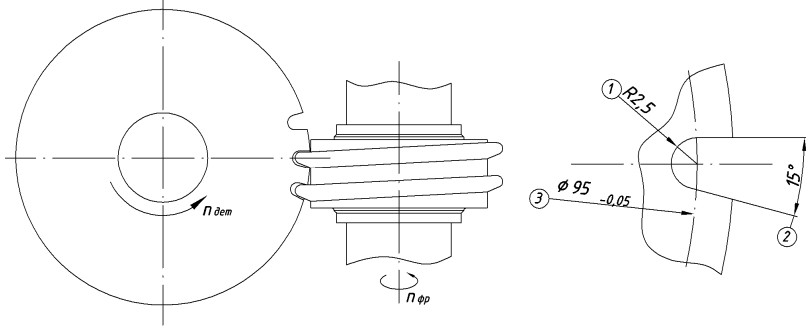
Операційний ескіз на операцію 035 зубофрезерну
